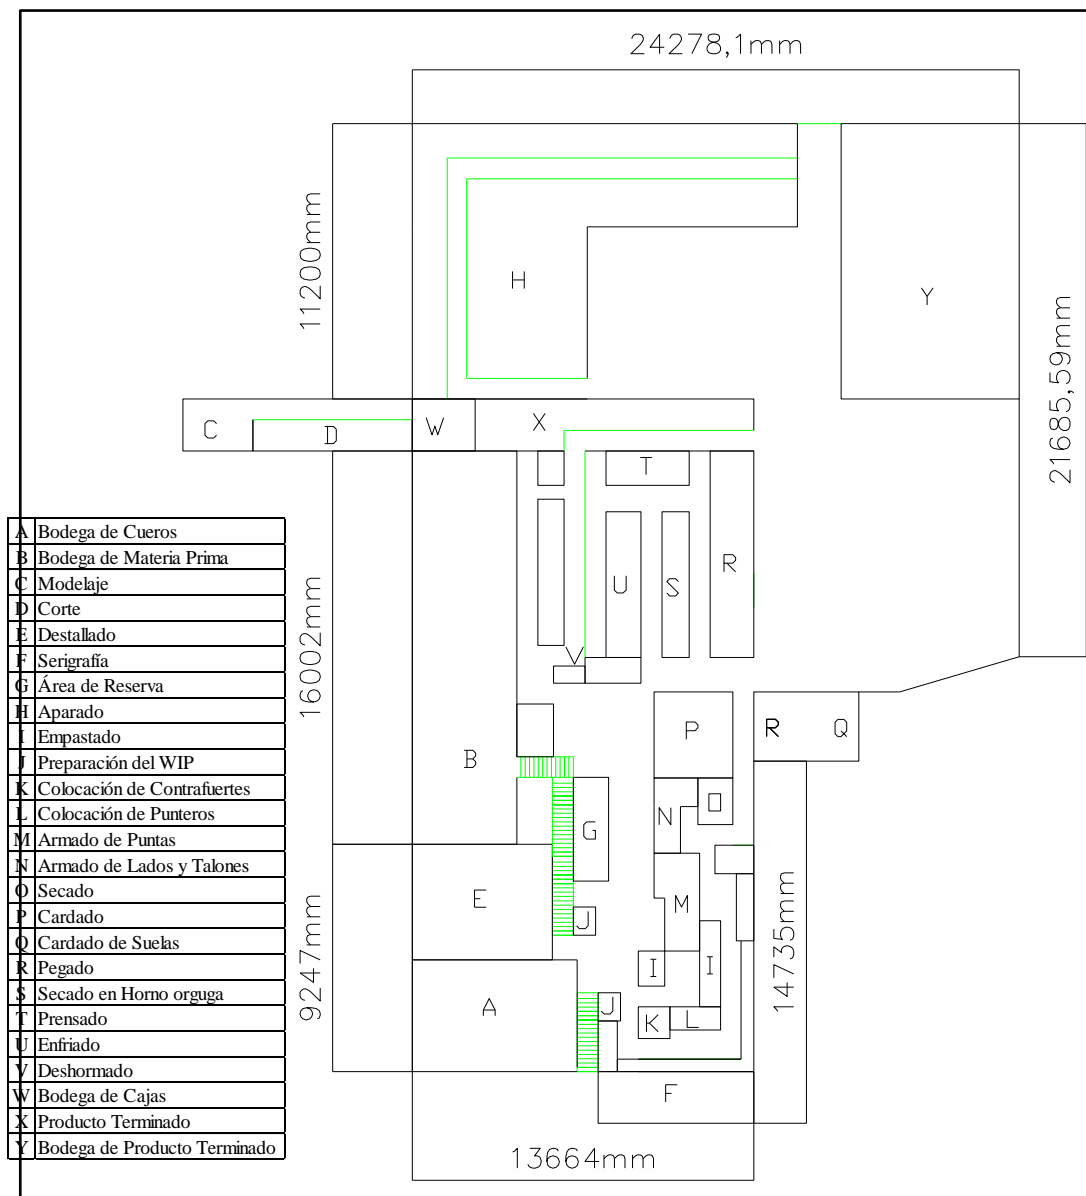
Layout actual de la Empresa Gamó's Dibujado en AutoCAD
